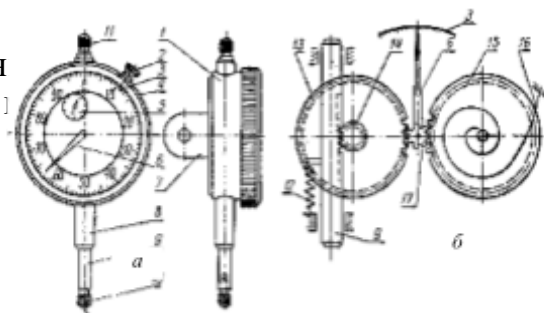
Індикатор нормального типу: 1 – корпус; 2 – стопорний гвинт; 3 – основна шкала; 4 – обичайка; 5 – шкала лічильника обертів великої стрілки; 6 – основна (велика) стрілка; 7 – вушко; 8 – втулка; 9 – вимірювальний стрижень; 10 – наконечник; 11 – головка; 12 – зворотня пружина; 13, 14, 15 і 17 – зубчасті колеса; 16 – спіральна пружина
